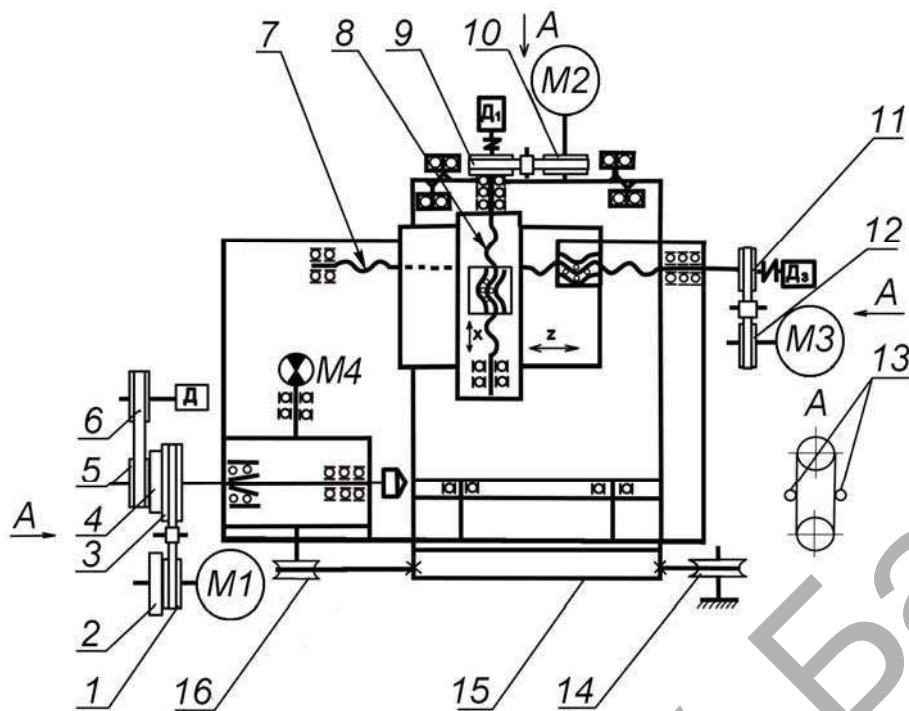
Кинематическая схема станка 1П420ПФ40
